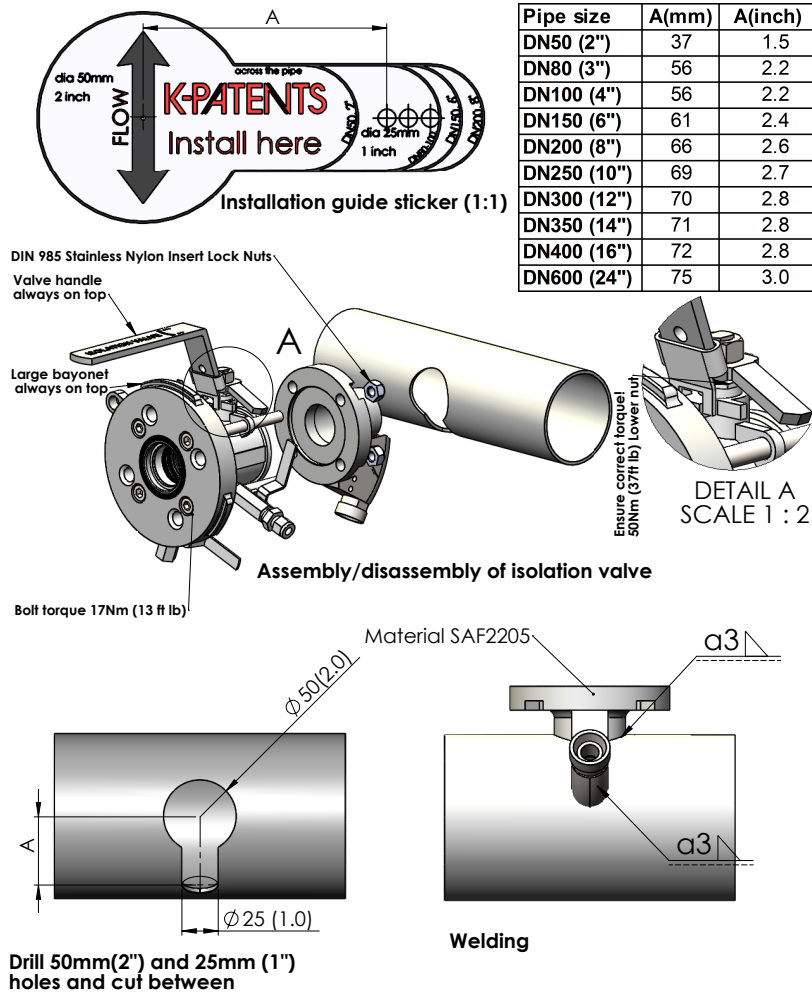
Soudage de la vanne d'isolement Safe-Drive™ à un tube horizontal
